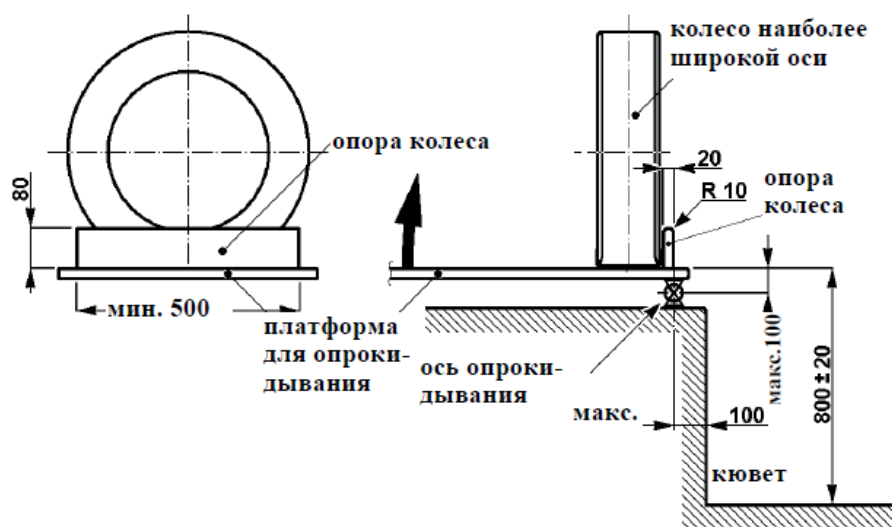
Стенд для испытания автобуса на опрокидывание по правилу ЕЭК ООН № 66
